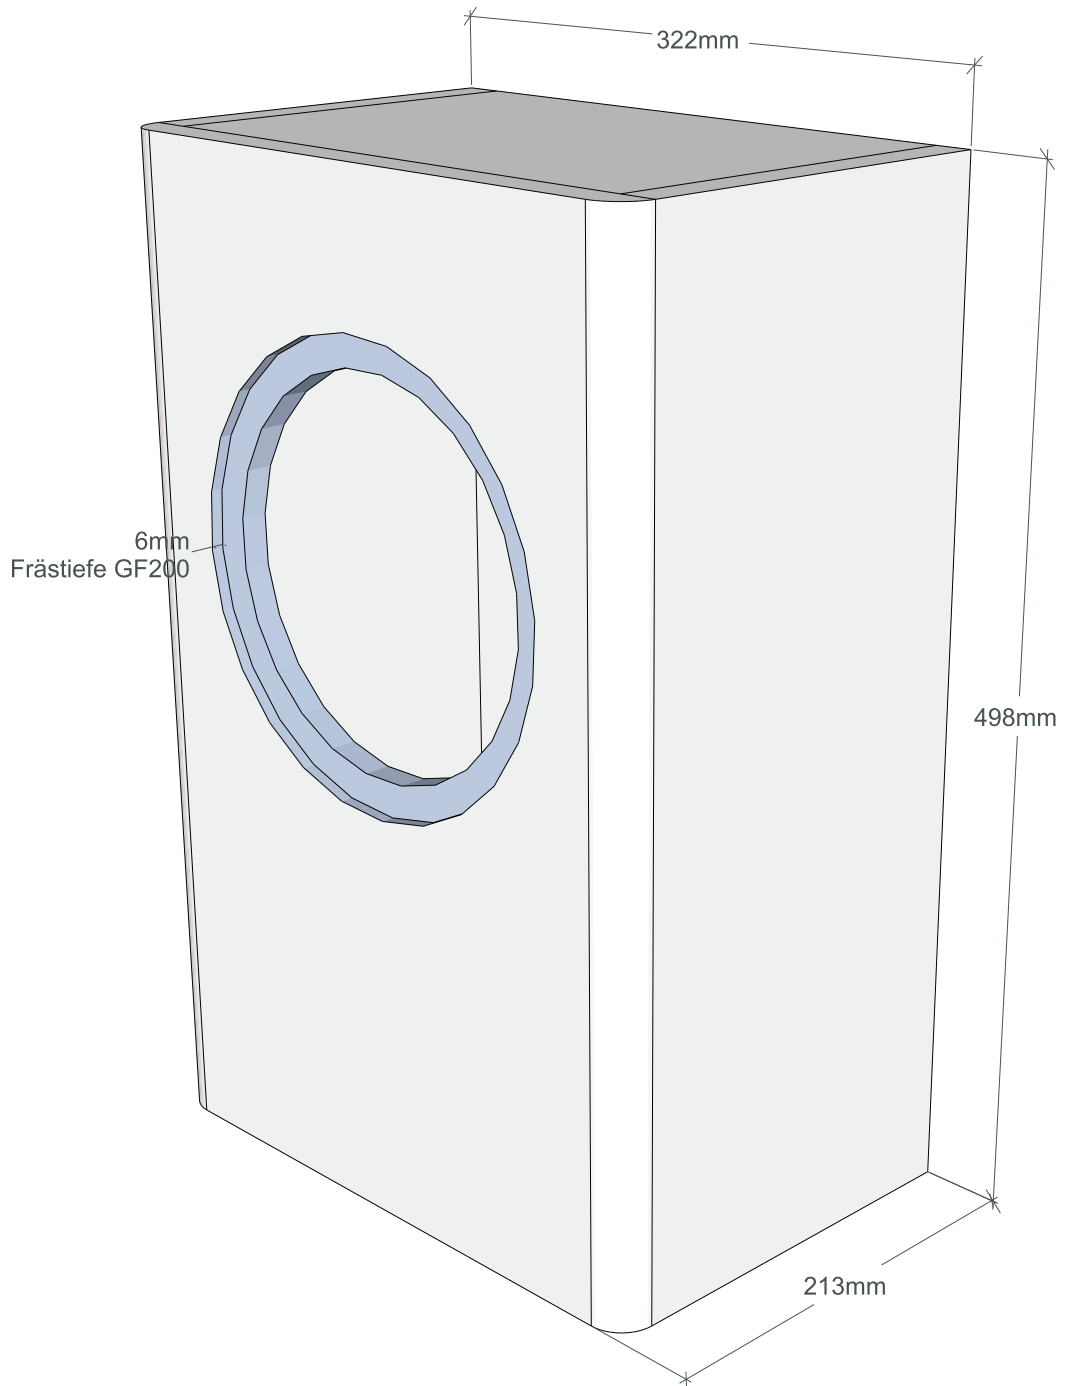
ISO Frontansicht geschlossenes 22,9l Gehäuse
